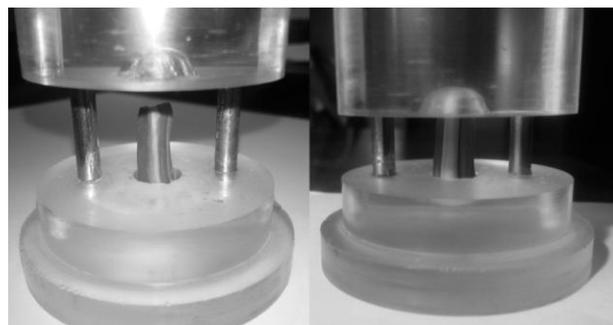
Заготовка из столбцов разноцветного пластилина установленная в штамп
